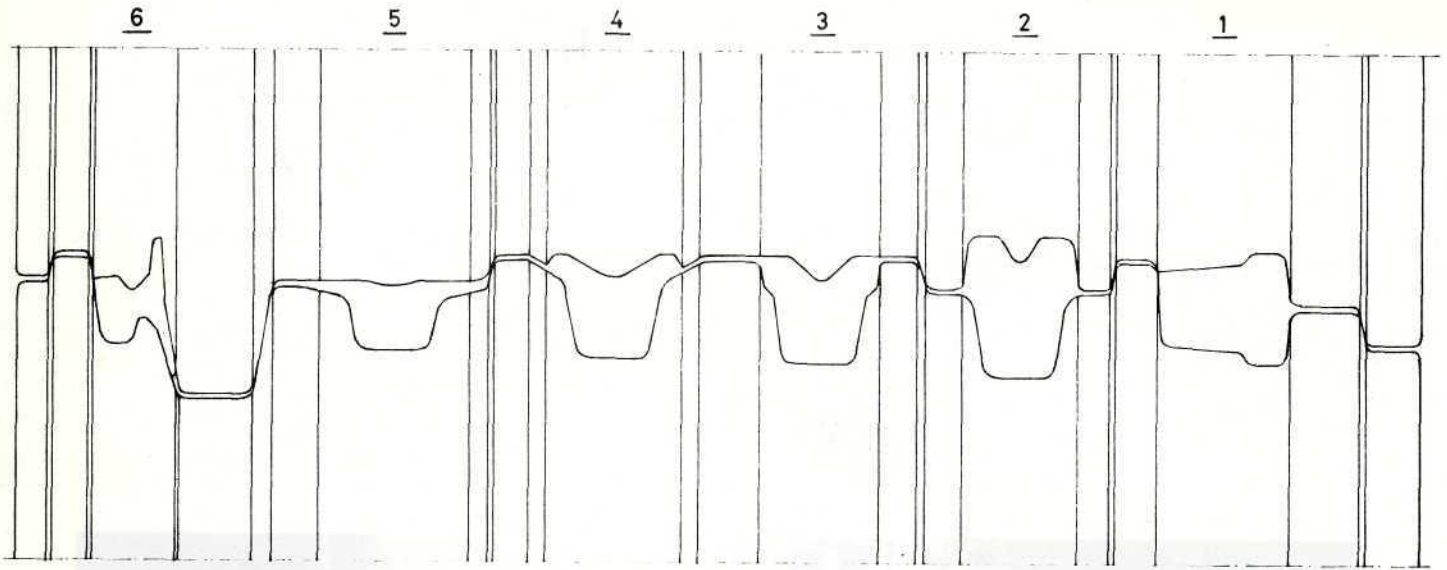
Algemeen overzicht van de railwalserij tijdens het gelijktijdig walsen van twee spoorstaven.
